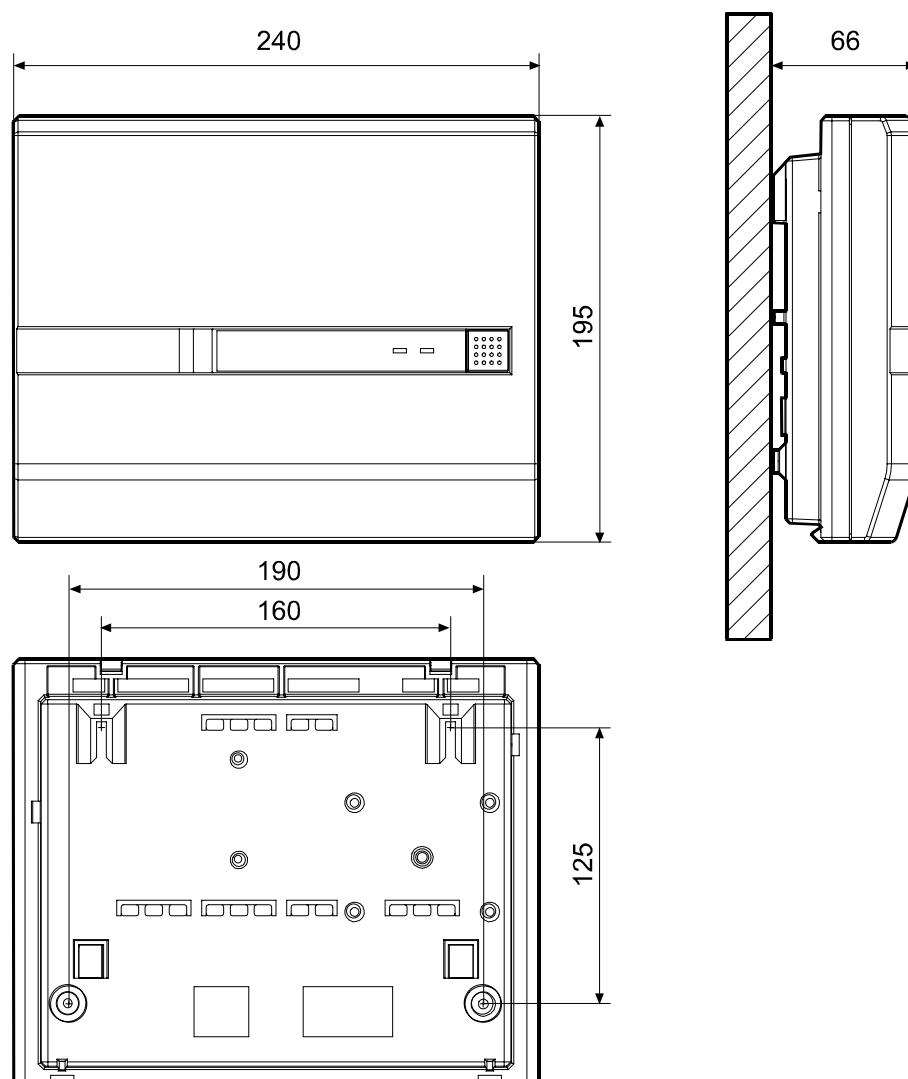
Габаритные размеры контроллера «Кронверк АТ+».
